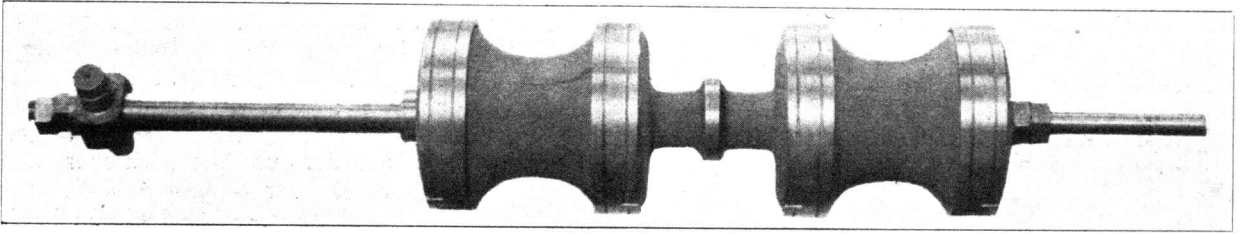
Kolbenschieber der 2 C Vierzylinder-Heißdampf-Schnellzuglokomotiven mit Schlepptender Nr. 71--74, gebaut von J. A. Maffei, München.
